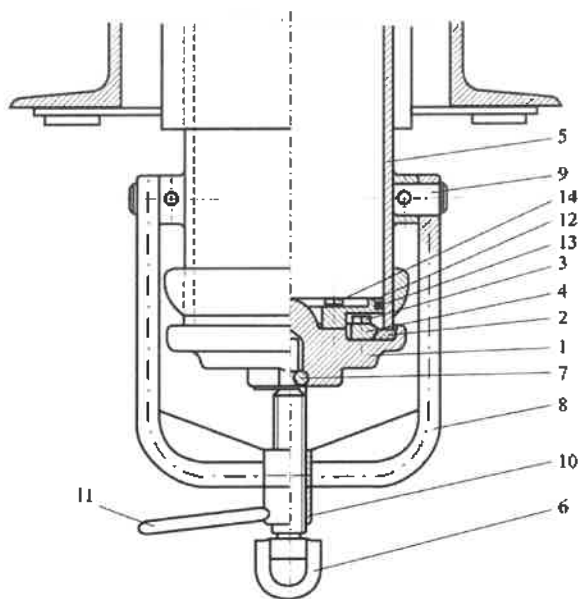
Усовершенствованная конструкция универсального сливного прибора [6]
